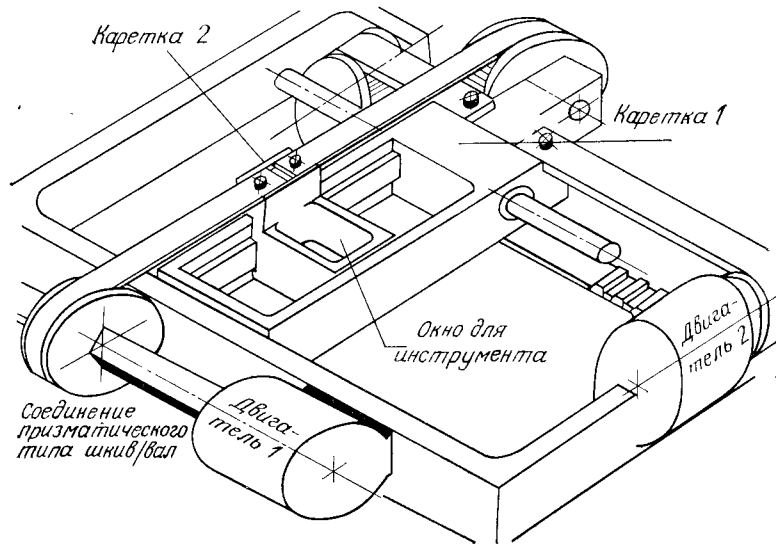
Принцип передачи движения двухкоординатного робота CADRATIC. (Фирма SORMEL.)
